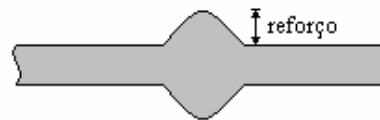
Perfil do material que compõe o tanque esférico com solda.
